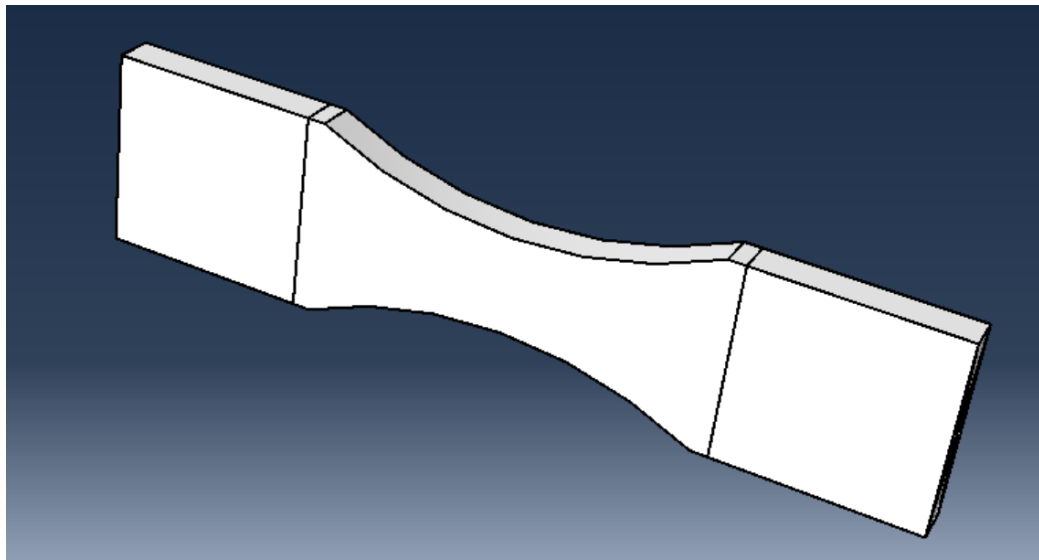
Les éprouvettes modélisées avec ABAQUS sans soudage.
